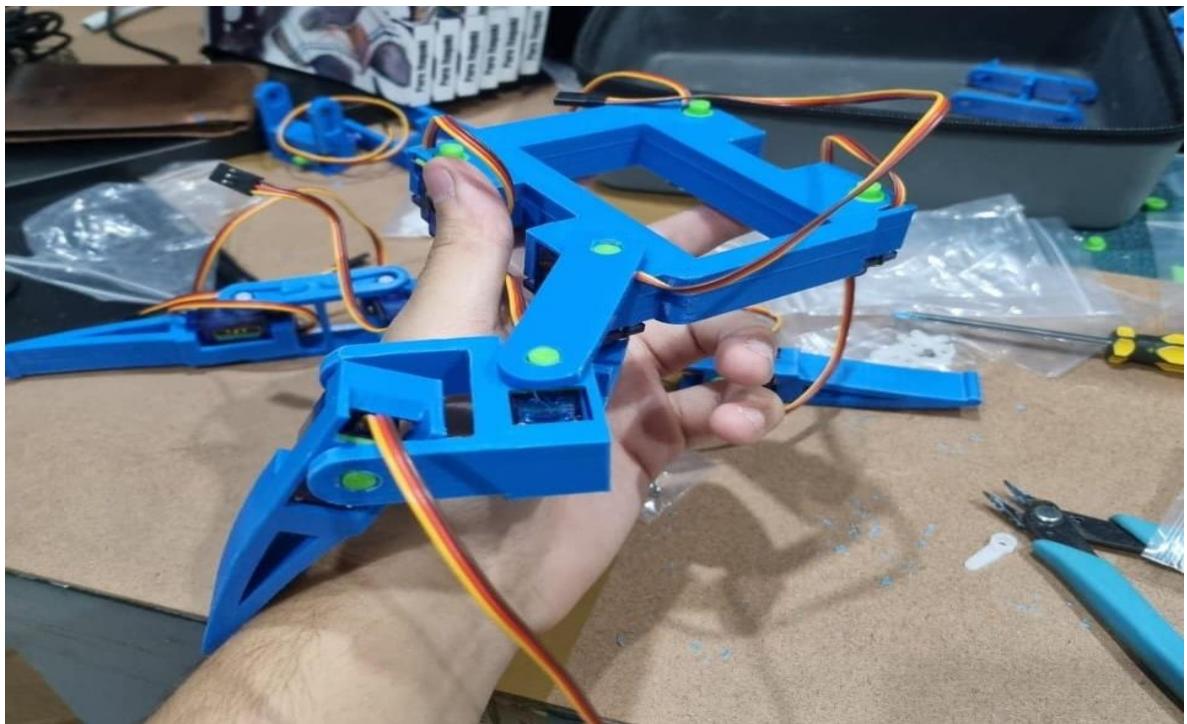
Partes do Robô Aranha impressos na Impressora 3D - Fonte: Próprio autor
